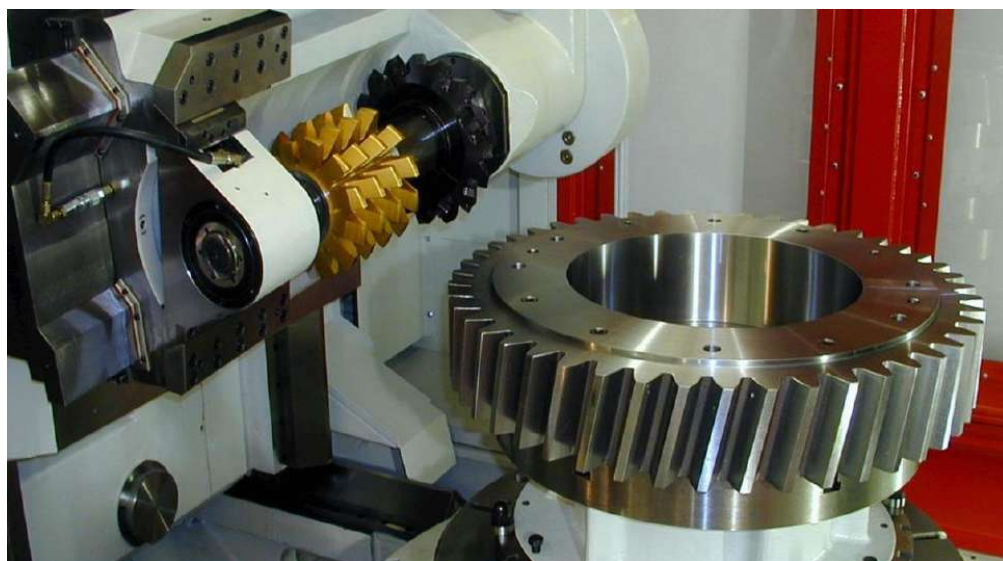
Процесс зубофрезерования на станке HGH-180
